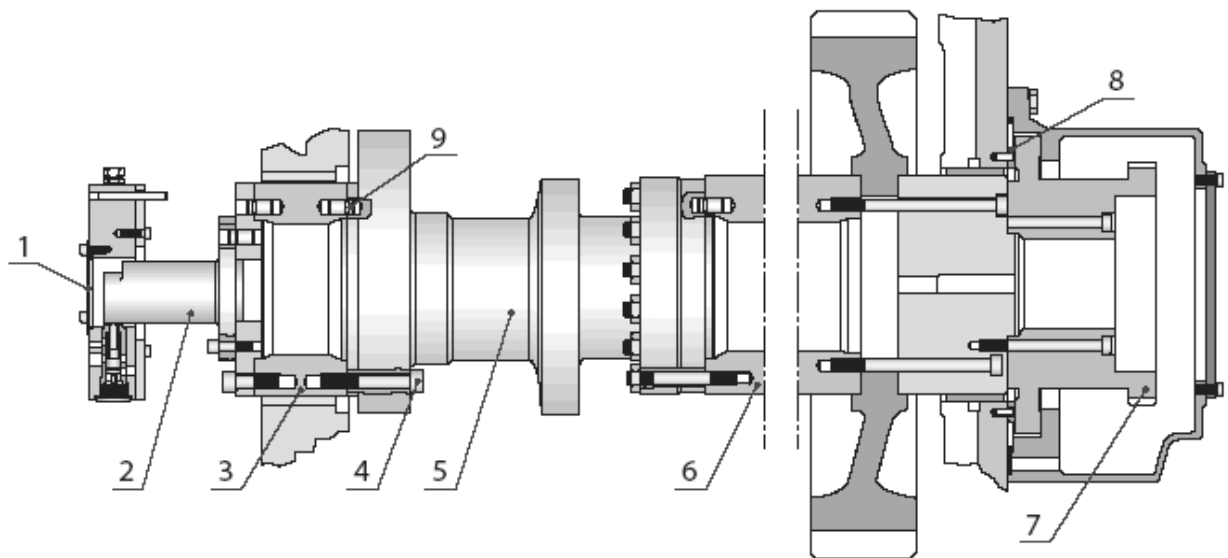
Розподільний вал: 1 – кришка; 2 – подовжувальна секція для розподільника пускового повітря; 3 – підшипникова цапфа; 4 – гвинт; 5 – секція розподільного вала; 6 – подовжувач; 7 – шестерня для приво­ду регулятора; 8 – упорний підшипник; 9 – напрямний штифт
